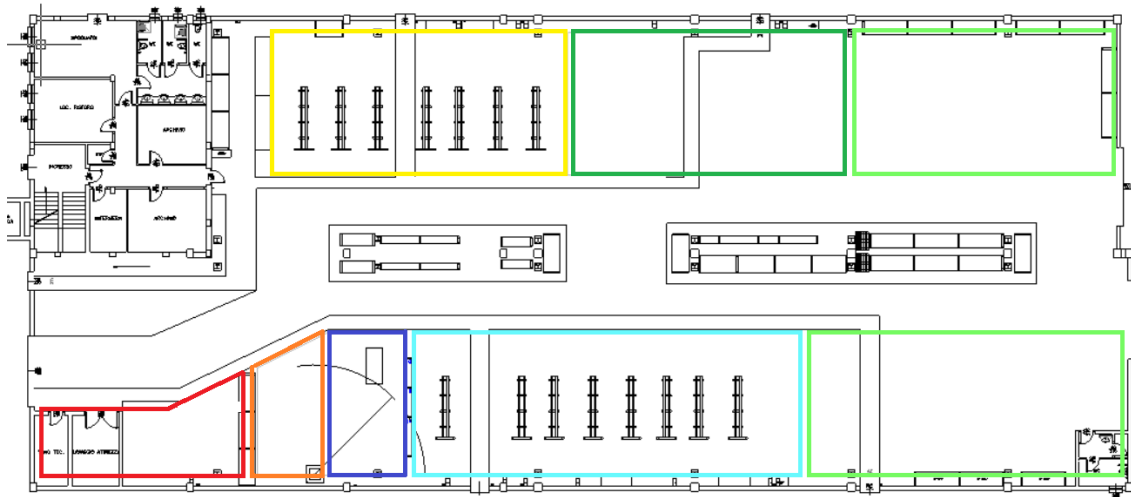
Layout in pianta dello stabilimento produttivo di via Meucci 22
